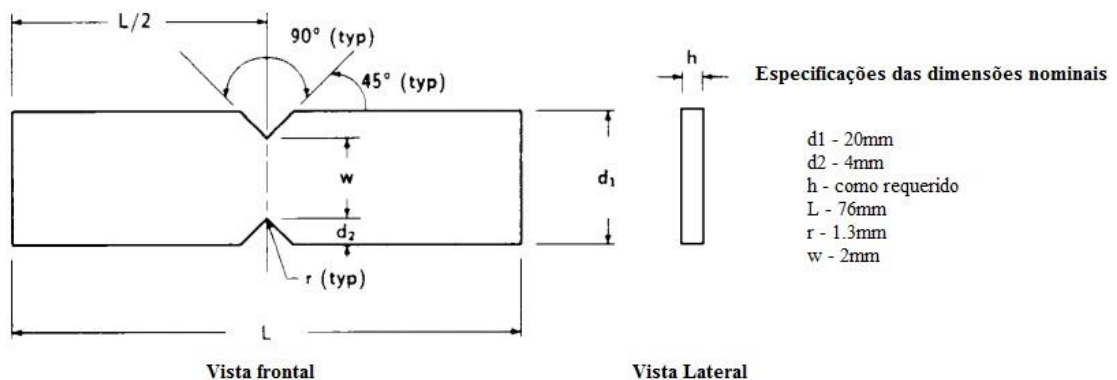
Geometria e dimensões (mm) do provete para o ensaio Iosipescu (adaptado de [26])
